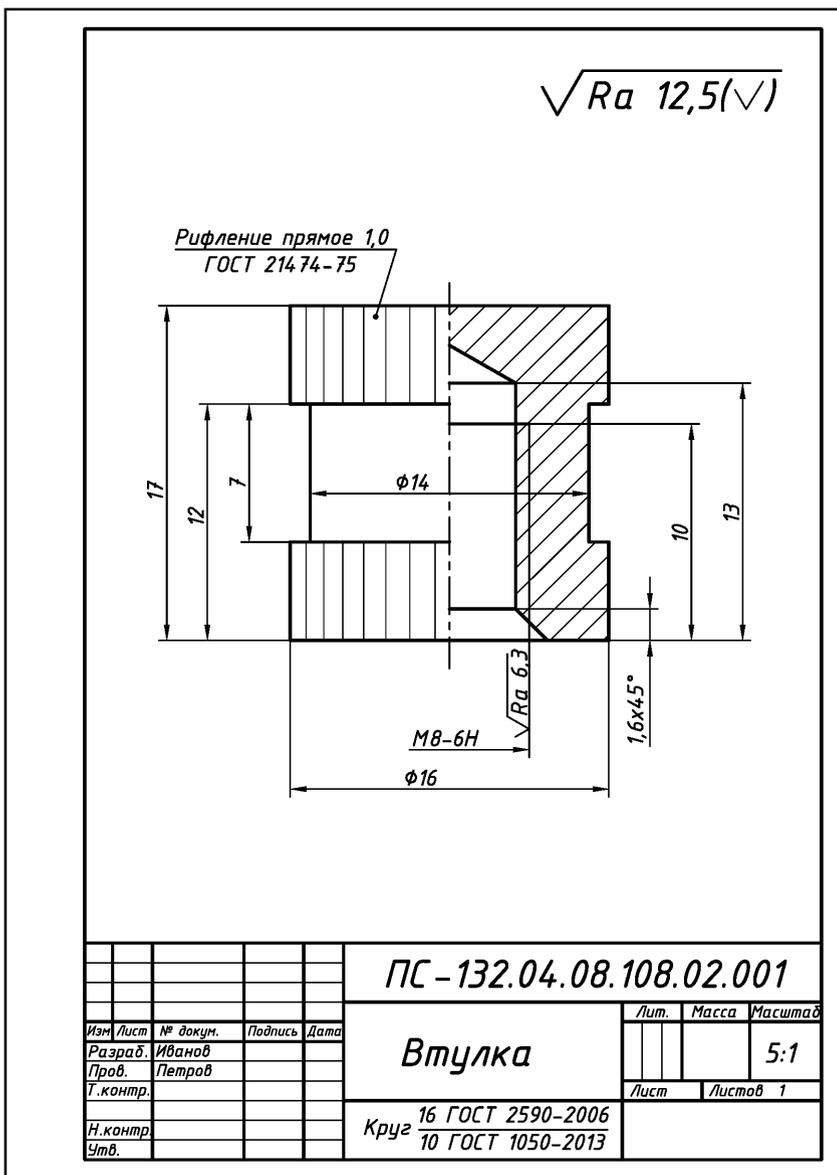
Оформление рабочего чертежа детали «Втулка» армированного изделия «Рукоятка» (рис. 1.91)
